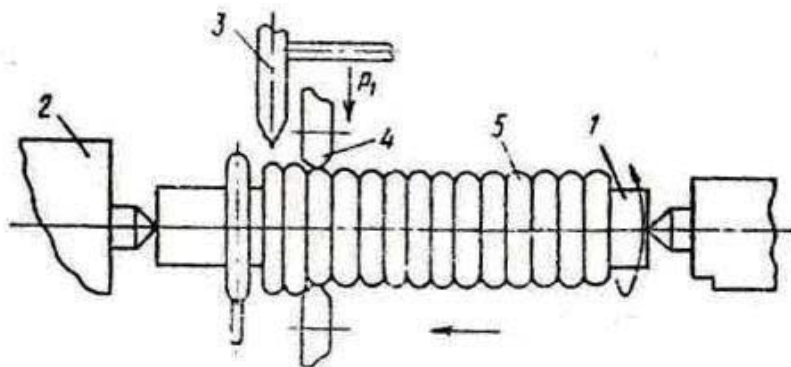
Схема разработанного процесса наплавки и предварительного деформирования поверхностного слоя.
